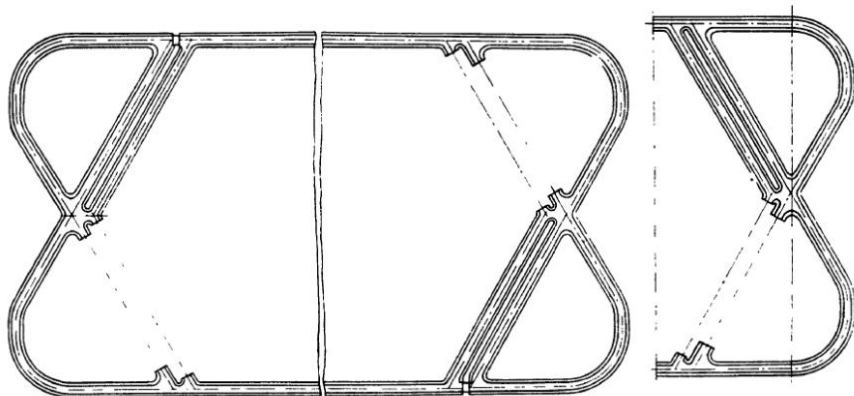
Резиновая прокладка для пластин 0,5-Е
